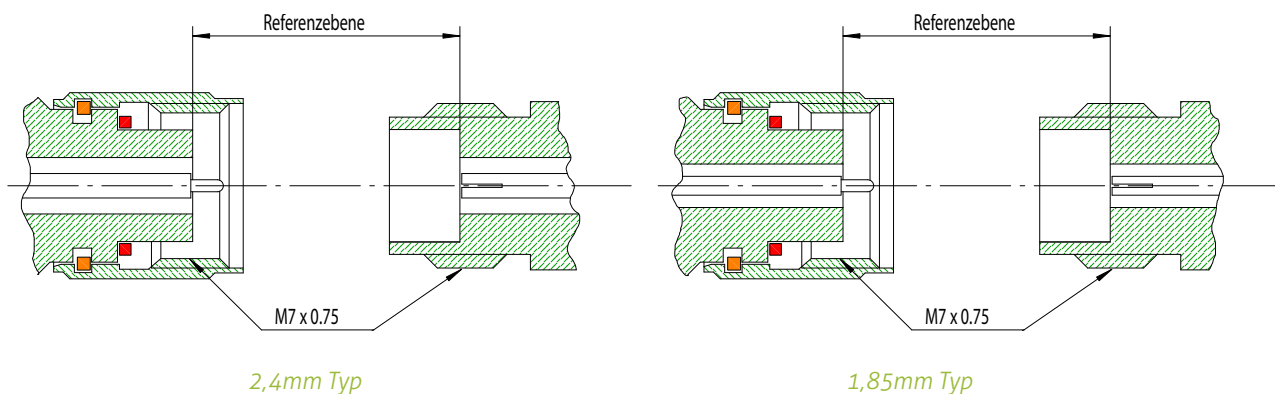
Schnittzeichnungen des 2,4mm und 1,85mm-Steckers
